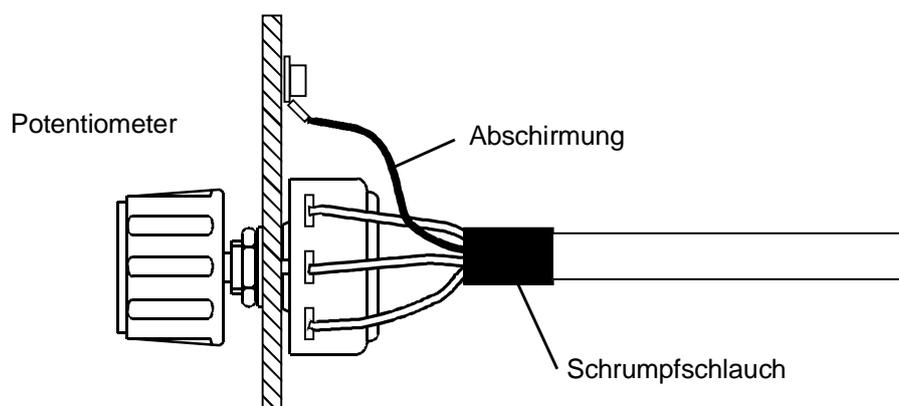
Beispiel einer Schirmbefestigung ohne Stecker
